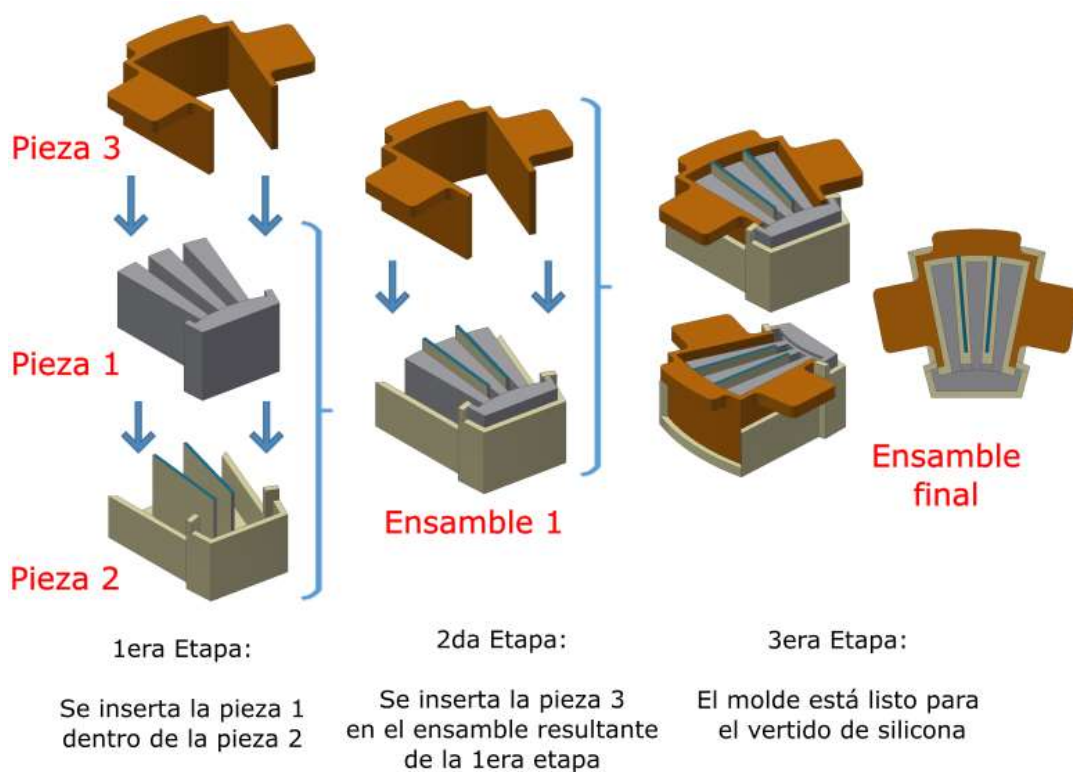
Ensamble final del molde para el cuerpo del actuador blando
